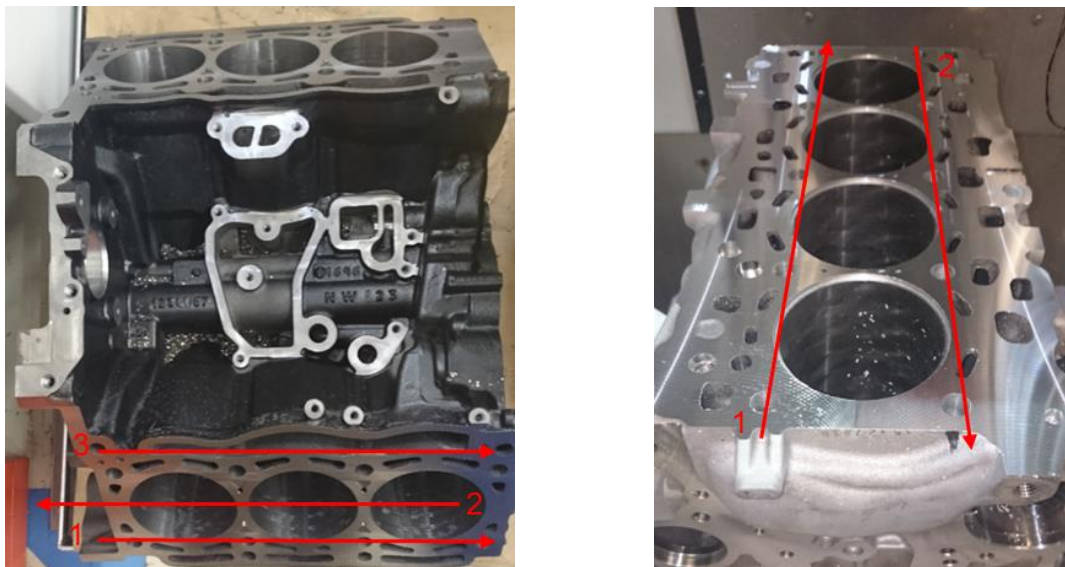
Bearbeitete Zylinderkurbelgehäuse der 3.Versuchsreihe
